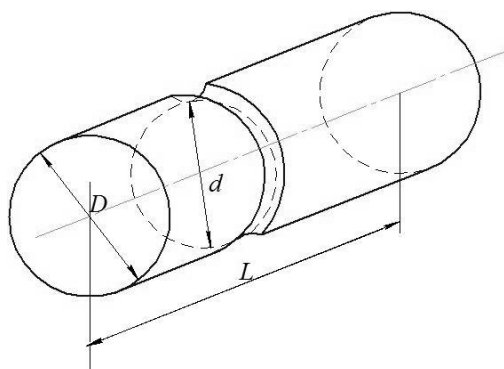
Цилиндрический образец с круговым надрезом полукруглого профиля
